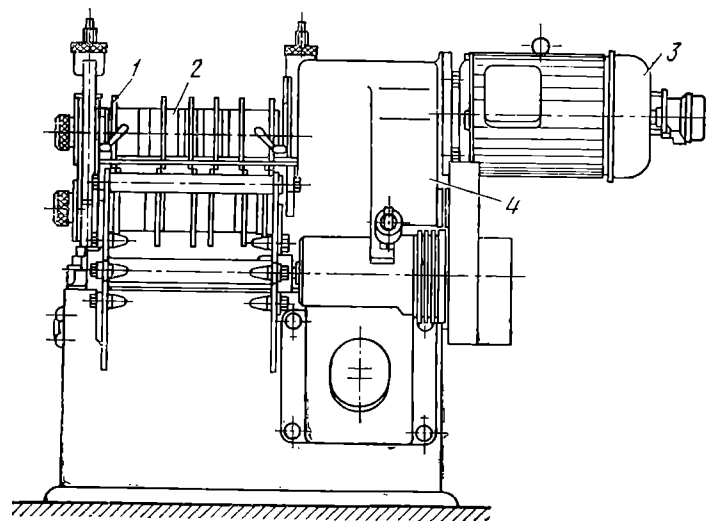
Дисковые ножницы с цилиндрическими ножами
